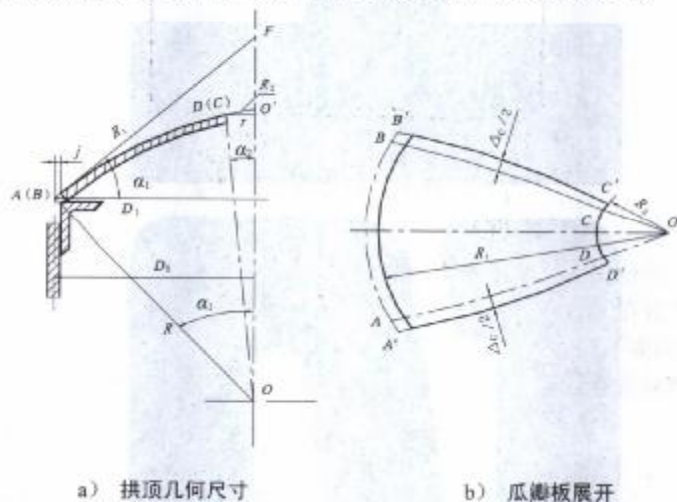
拱顶的几何尺寸及瓜瓣板尺寸
